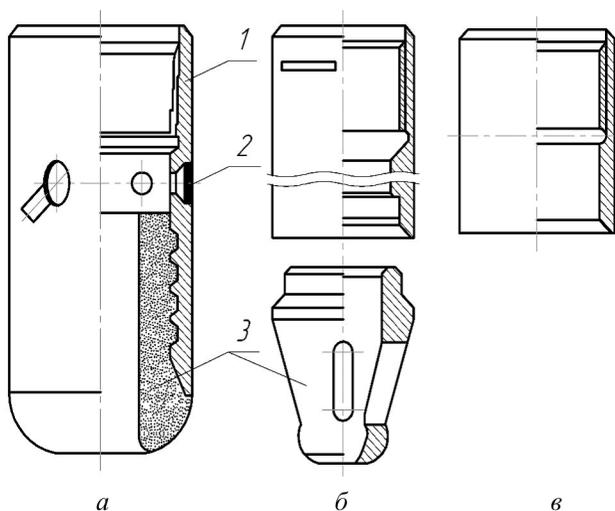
Башмаки колонные типов БКМ (а), БП с чугунной направляющей насадкой (б) и Б (в): 1 – корпус; 2 – заглушка; 3 – направляющая насадка
